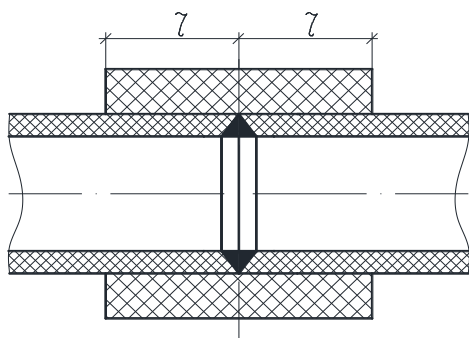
Конструктивные элементы шва сварного соединения (шов НС2)
